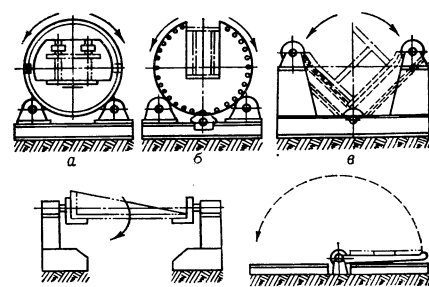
Кантователи: а — роликовый; б — цевочный; в — цепной; г — цапфовый; д — рычажный.
